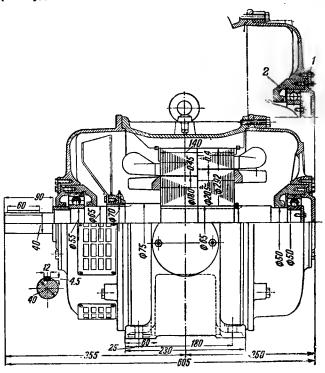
Асинхронный двигатель на шарикоподшипниках.
